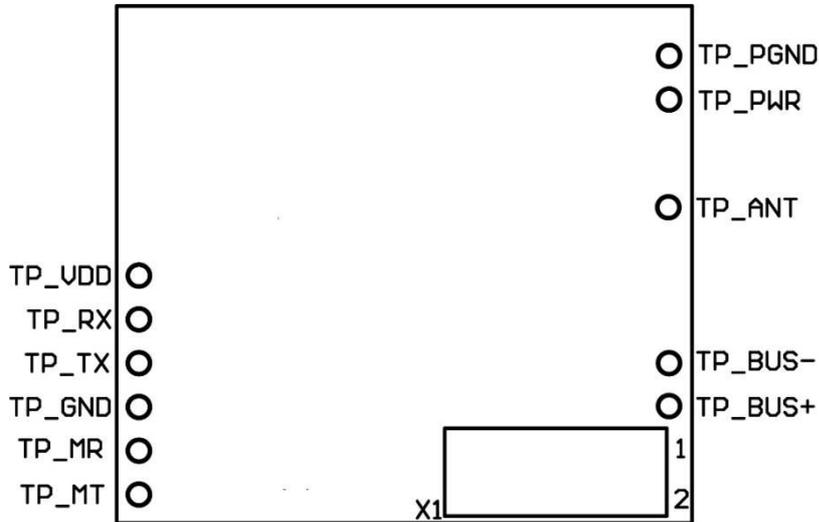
Draufsicht auf MBUS-M13 mit Anschlüssen
